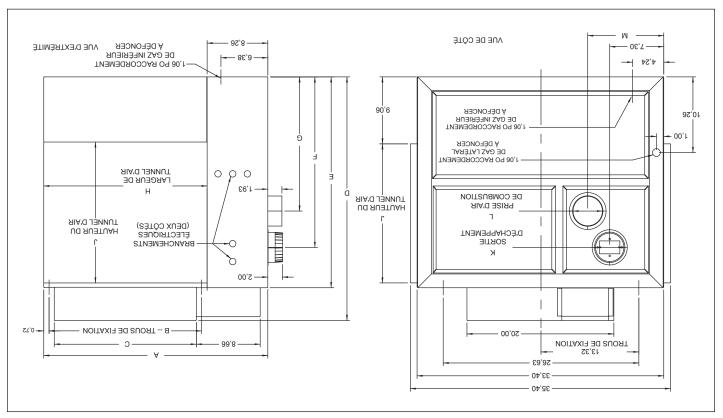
Dimensions de la chaudière canalisée d'intérieur à combustion séparée (toutes dimensions en pouces)
